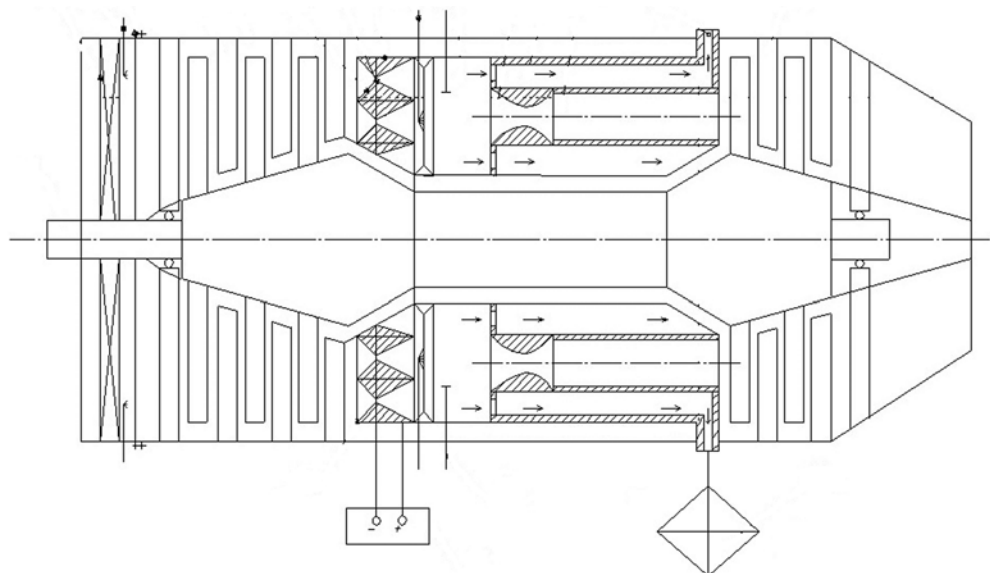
Газотурбинный двигатель с паровыми форсунками
